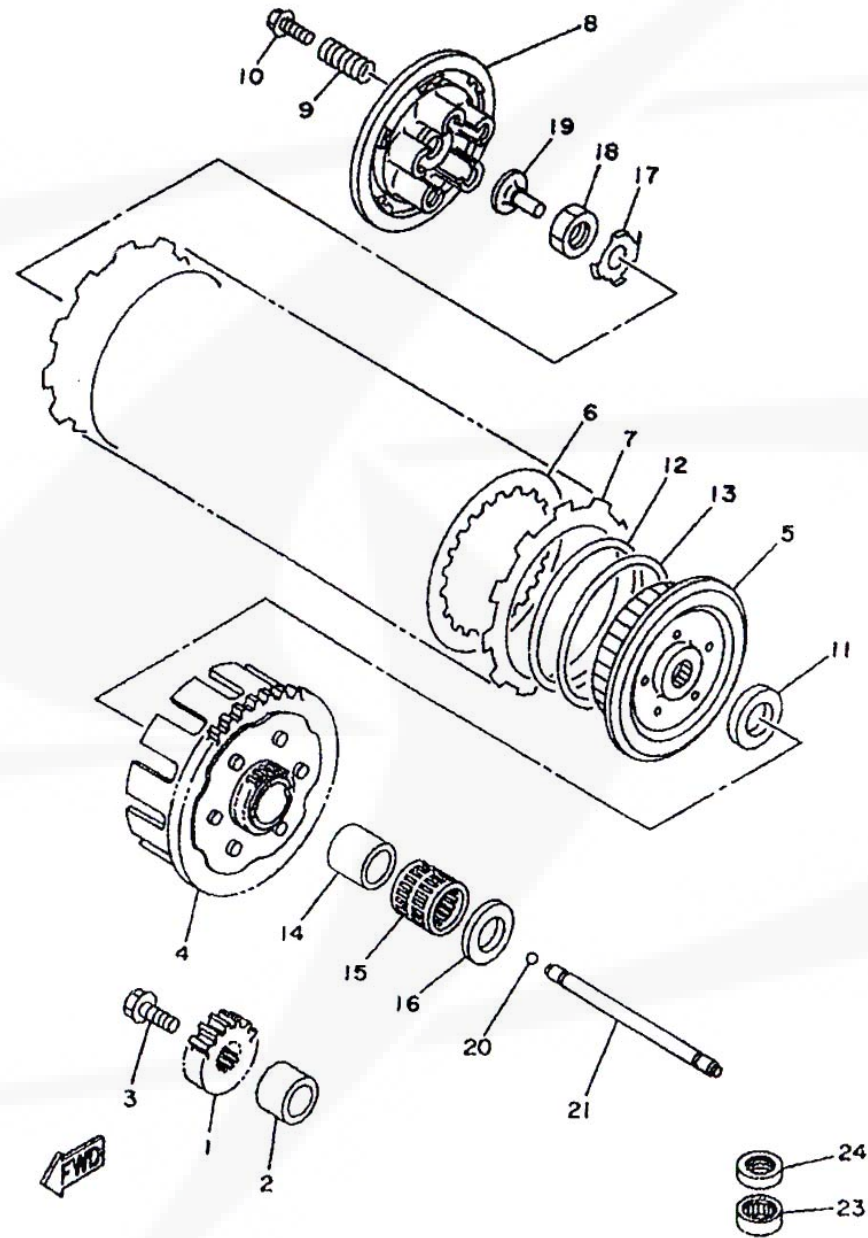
EMBRAYAGE / CLUTCH / EMBRAGUE
